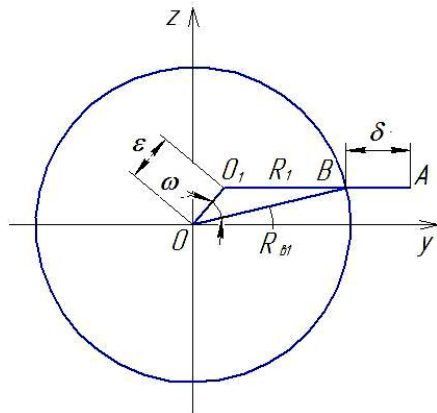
Поперечний переріз корпусу та його розташування щодо опорної лінії
